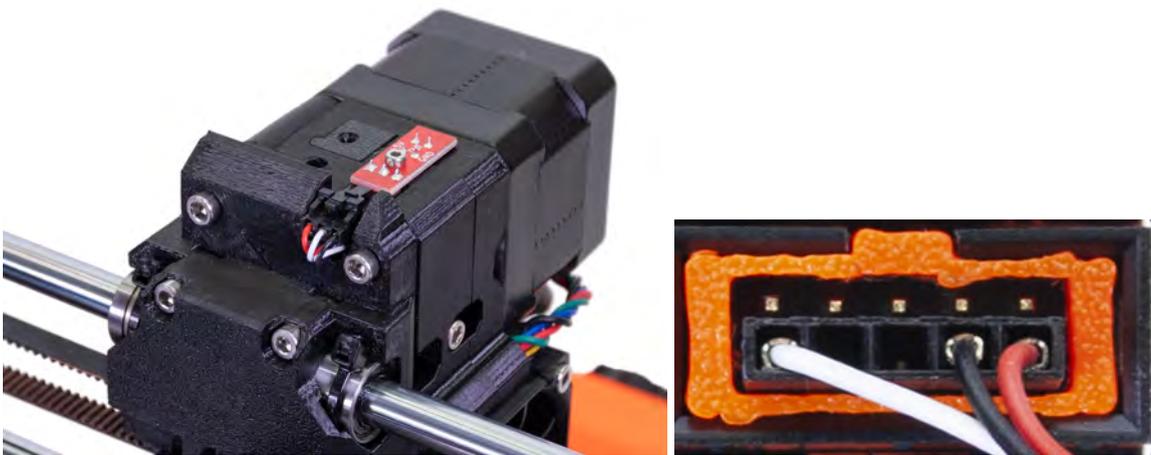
Korrekt angeschlossener und sitzender Filamentsensor
